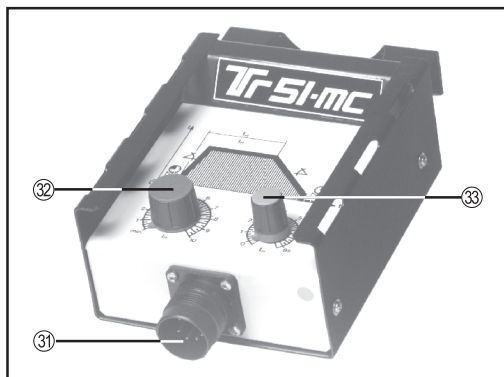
Mando a distancia para soldadura por puntos TIG TR 51 mc
